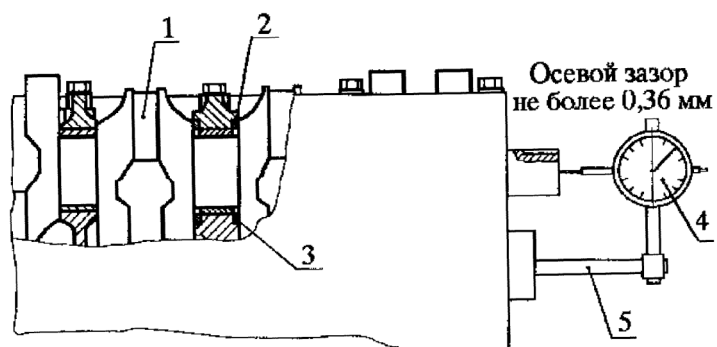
Проверка осевого зазора коленчатого вала:
